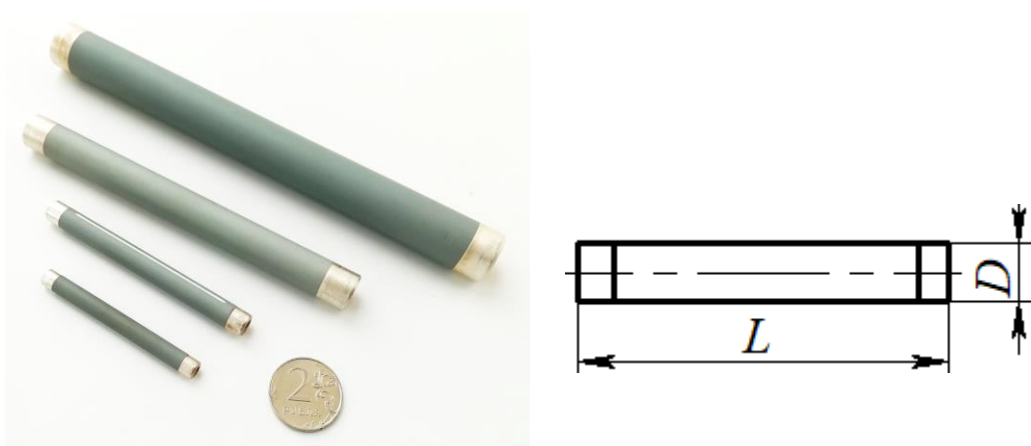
Резистор типа P1-69: внешний вид и основные размеры.
